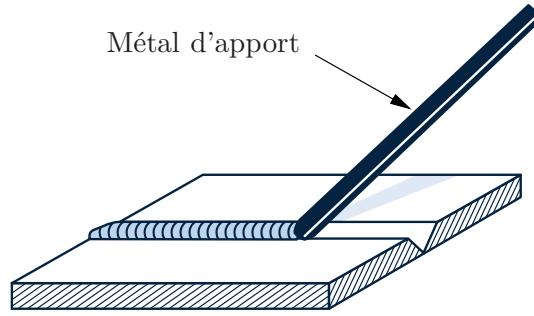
Soudage avec apport de matière dans un chanfrein ©Böhler Welding [112].
